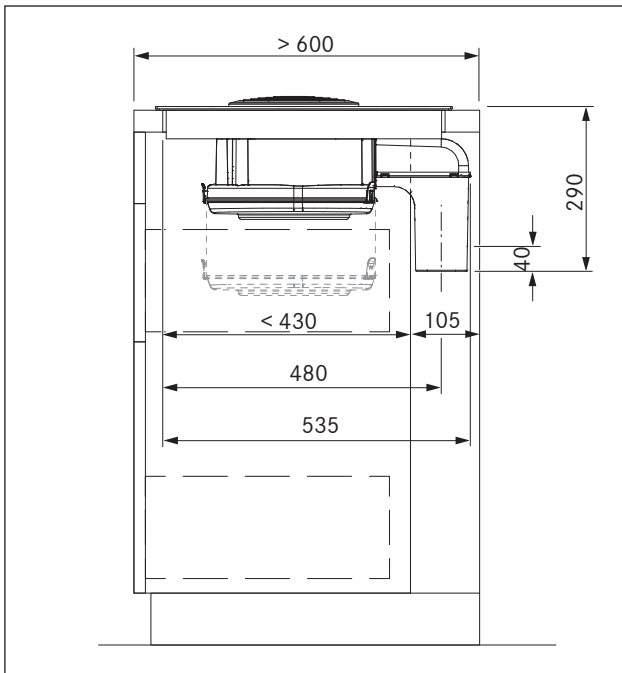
Dimensiones de montaje en aire de salida, profundidad de la encimera 600 mm
